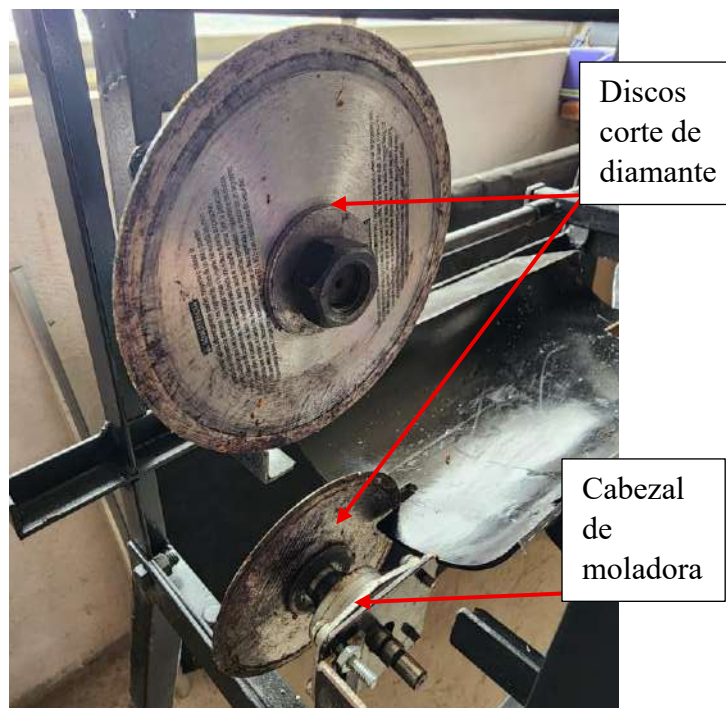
Sistema de corte seleccionado para la desvainadora de cacao
